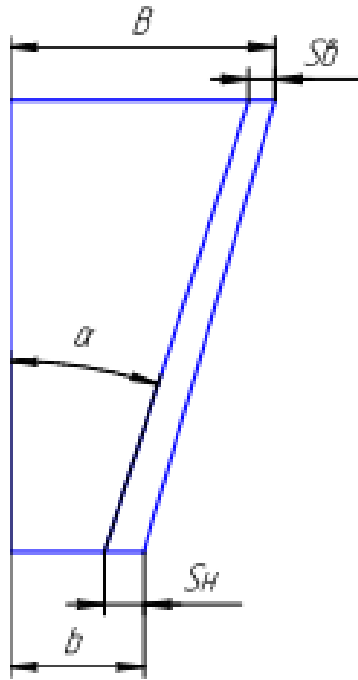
Схема для визначення ходу рухливої щоки
